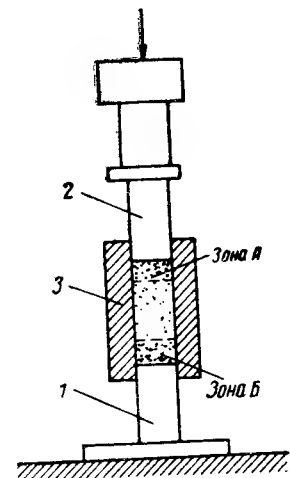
Схема двустороннего прессования с плавающей (свободноподвижной) формой
